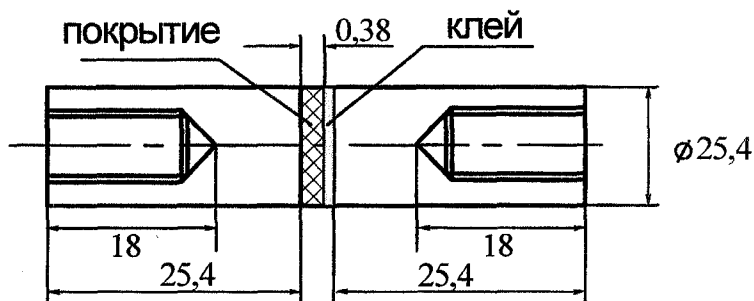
Образец для испытаний по ASTM C633-01
